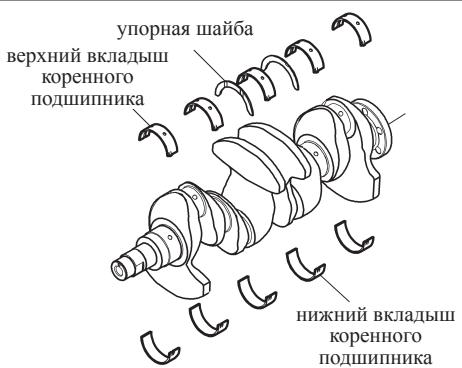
Проверка коленчатого вала и вкладышей коренных подшипников
